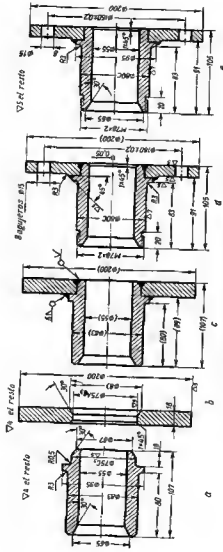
Dibujo industrial de uniones soldadas:
